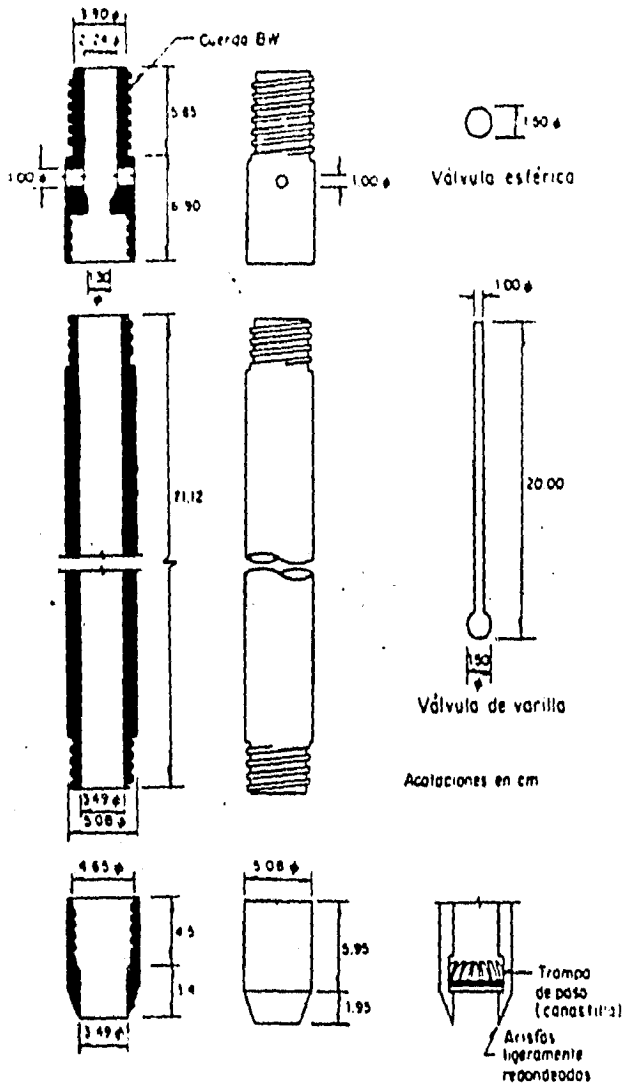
CORTE TRANSVERSAL DEL PENETRÓMETRO DINÁMICO TIPO ESTÁNDAR (REF.1,2,7)
